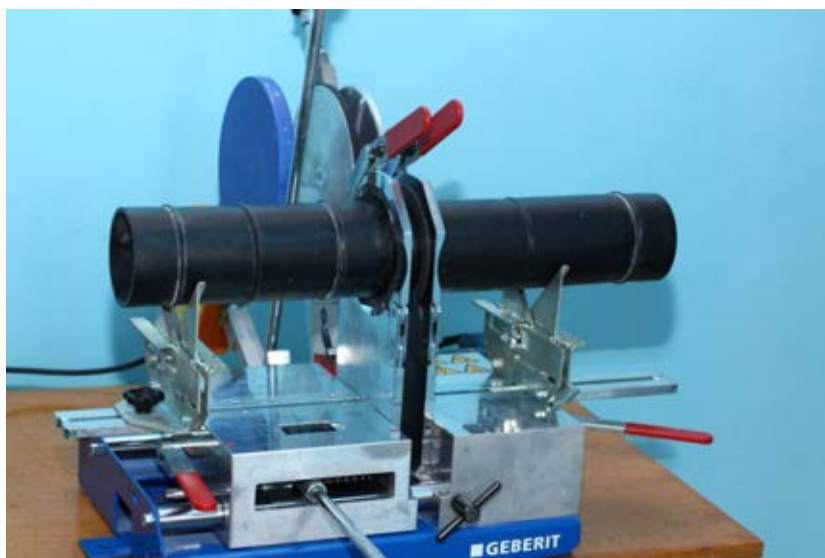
Зварювальний пристрій для контактного стикового зварювання труб
